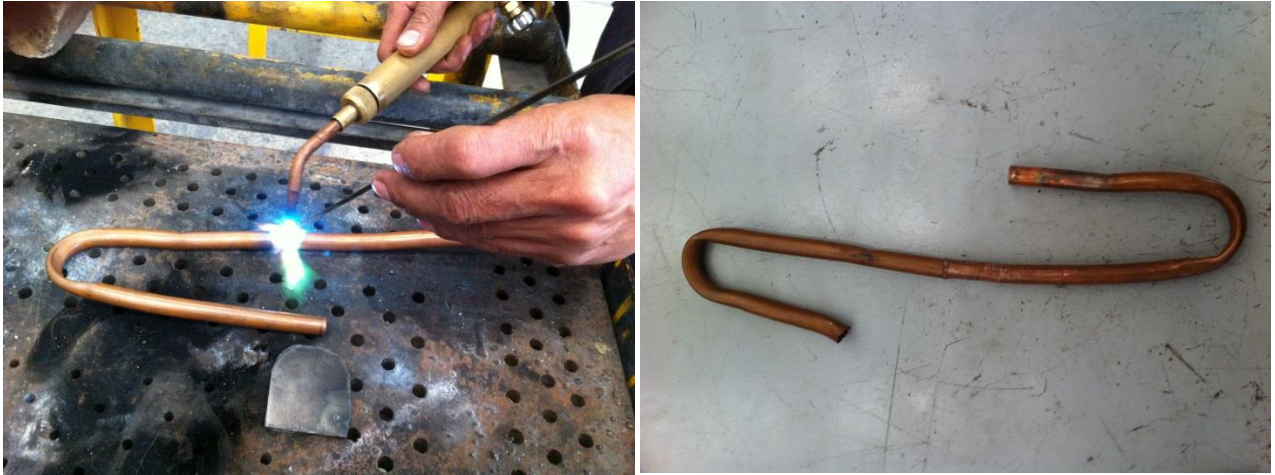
Proceso de soldadura para ensamblar las placas del condensador y del evaporador
